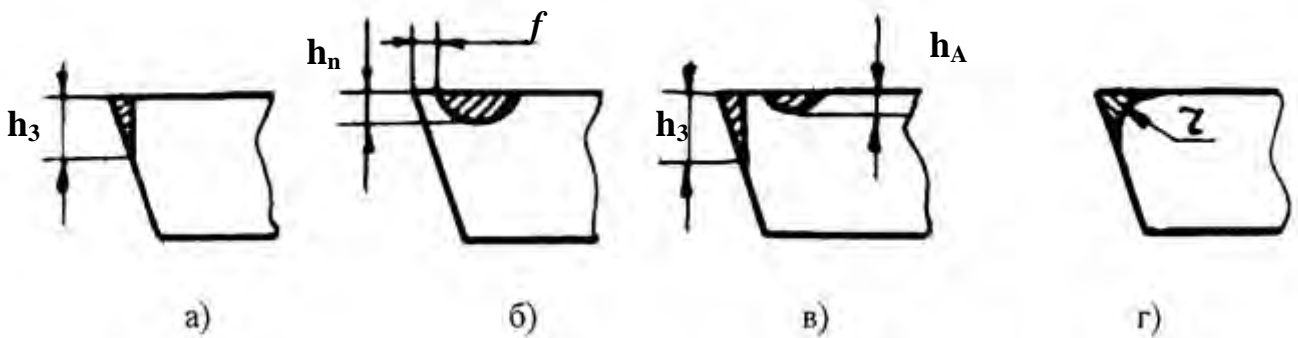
Основні форми зносу різальної частини інструменту: а-по задній поверхні; б-по передній поверхні; в-по задній і передній поверхнях; г-плавне заокруглення
